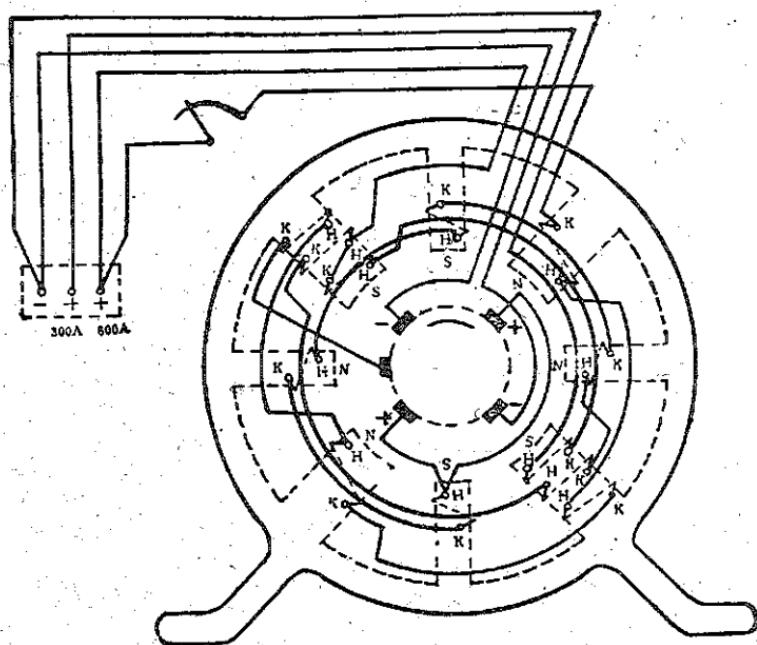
AX1—500型焊接发电机内部接线图（自换向器端视图）
